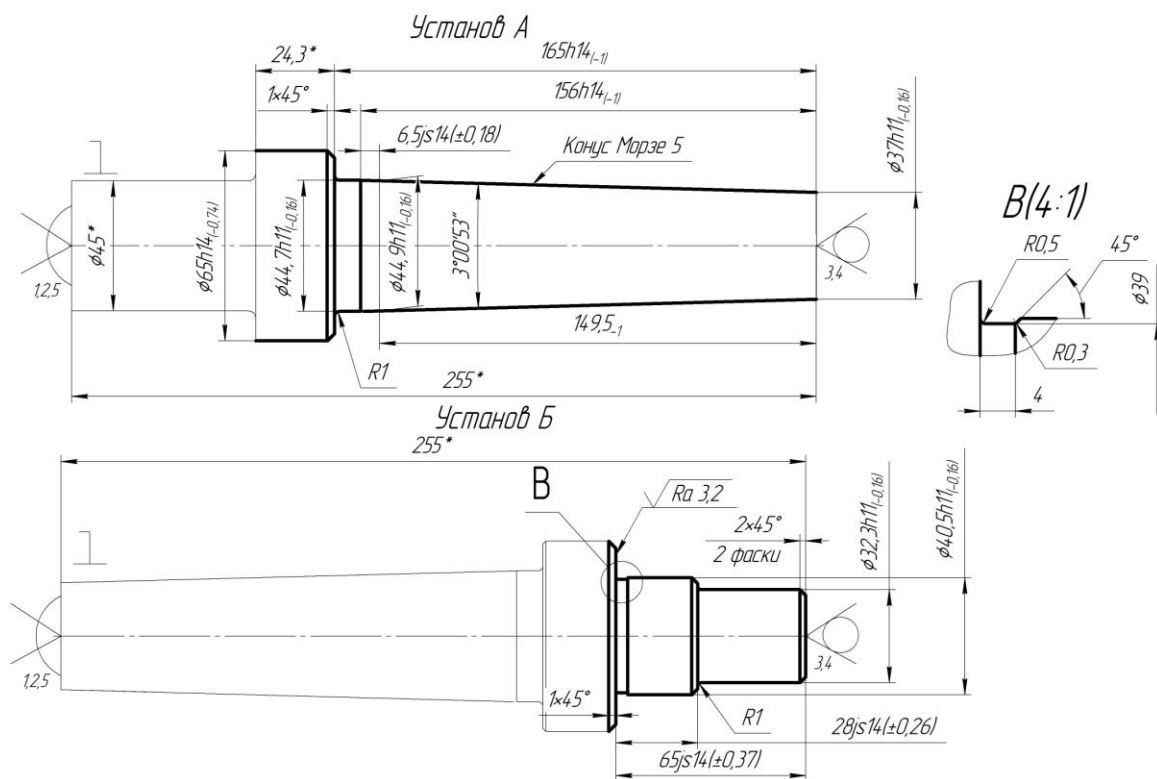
Схема базування заготовки на токарній з ЧПК операції (перший варіант)
